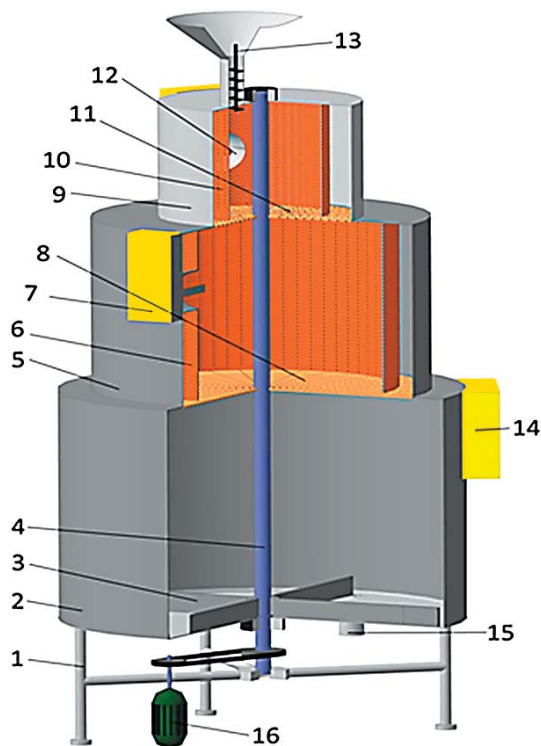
Установка с дифракционными поярусно расположенными цилиндрическими резонаторами
